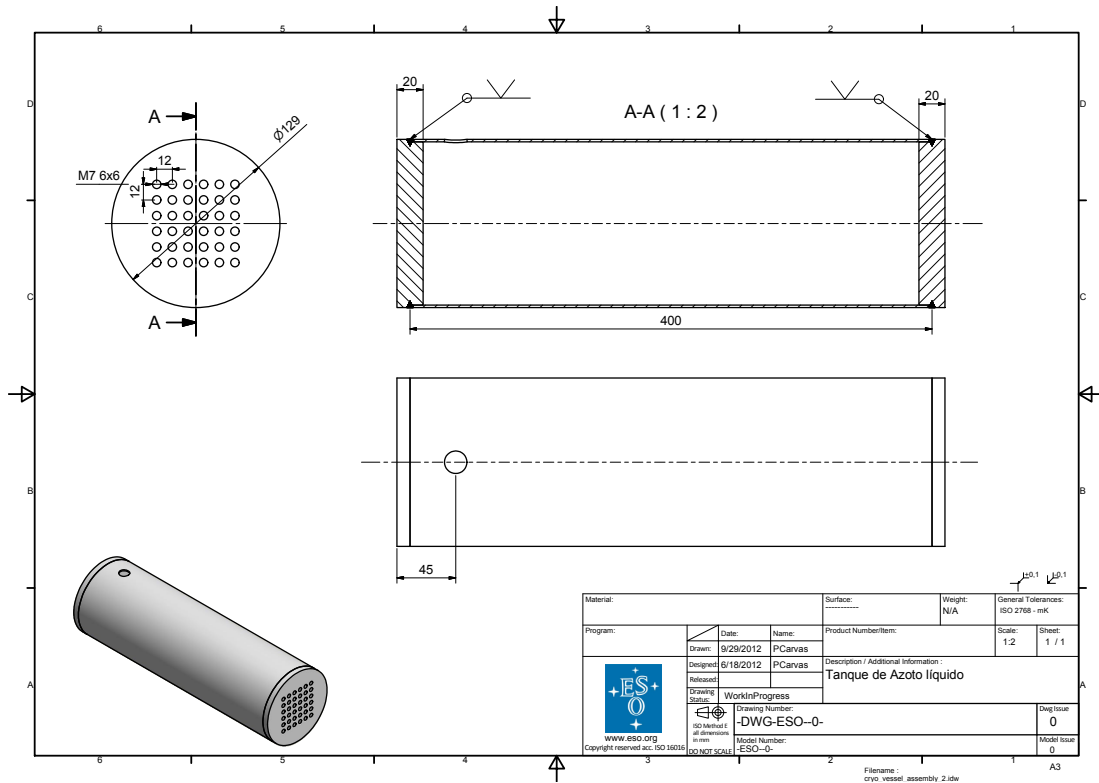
Desenho técnico do tanque de Azoto líquido.
